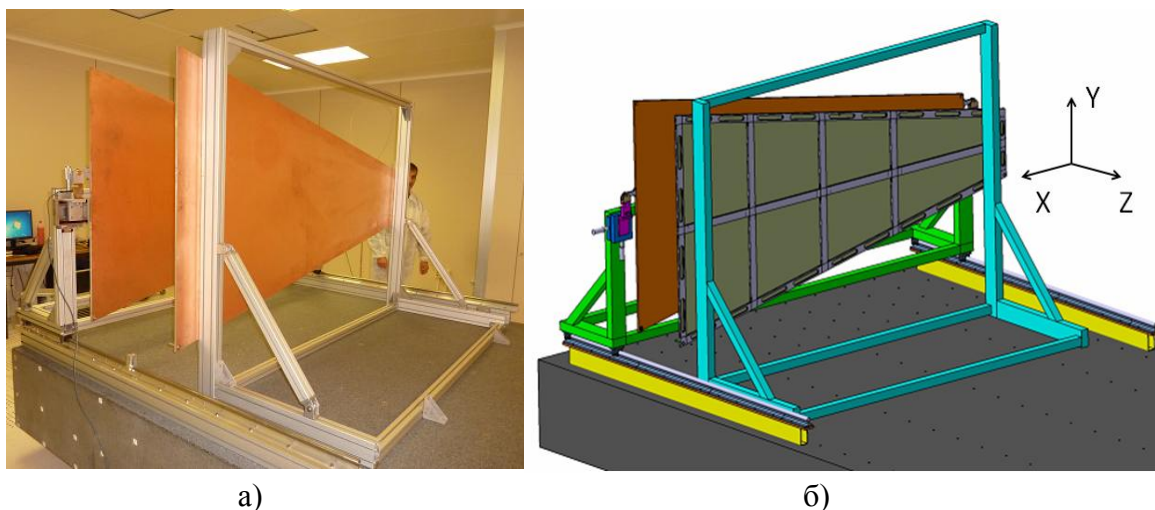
Механическое устройство для сборки квадруплета: а)фото, б) схема.
